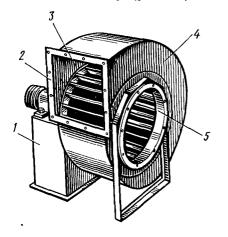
Радиальный (центробежный) вентилятор: 1— станина, 2— выхлопной патрубок, 3— ротор, 4— кожух вентилятора, 5— вса-
